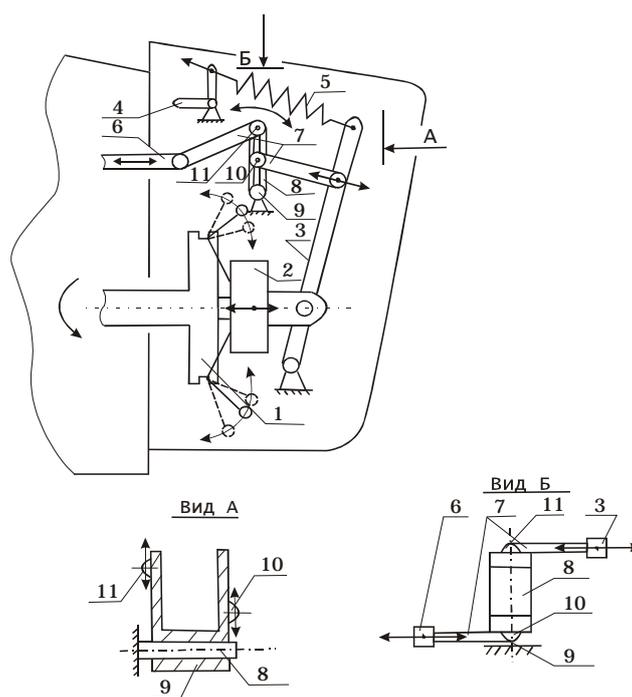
Система регулирования многотопливного дизеля: 1 – центробежный датчик; 2 – муфта; 3 – главный рычаг; 4 – рычаг управления; 5 – пружина; 6 – рейка; 7 – полутяги; 8 – вильчатый рычаг; 9 – дополнительный вал; 10, 11 – узлы соединения полутяг с вилкой
